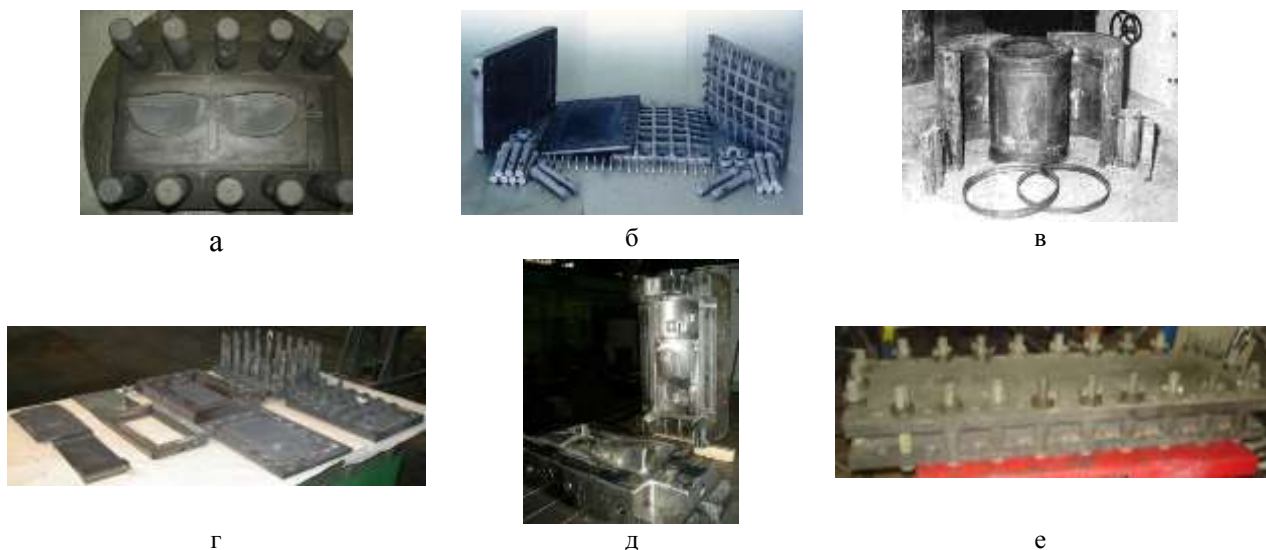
Технологические оснастки: а - оснастка для изготовления лицевых пластин для гольфа; б - оснастка для изготовления изделия «Wing Slat»; в - оснастка для изготовления узла «Корпус»; г и д оснастки для изготовления лопатки-имитатора; е - оснастка для изготовления узла «Крыло».
